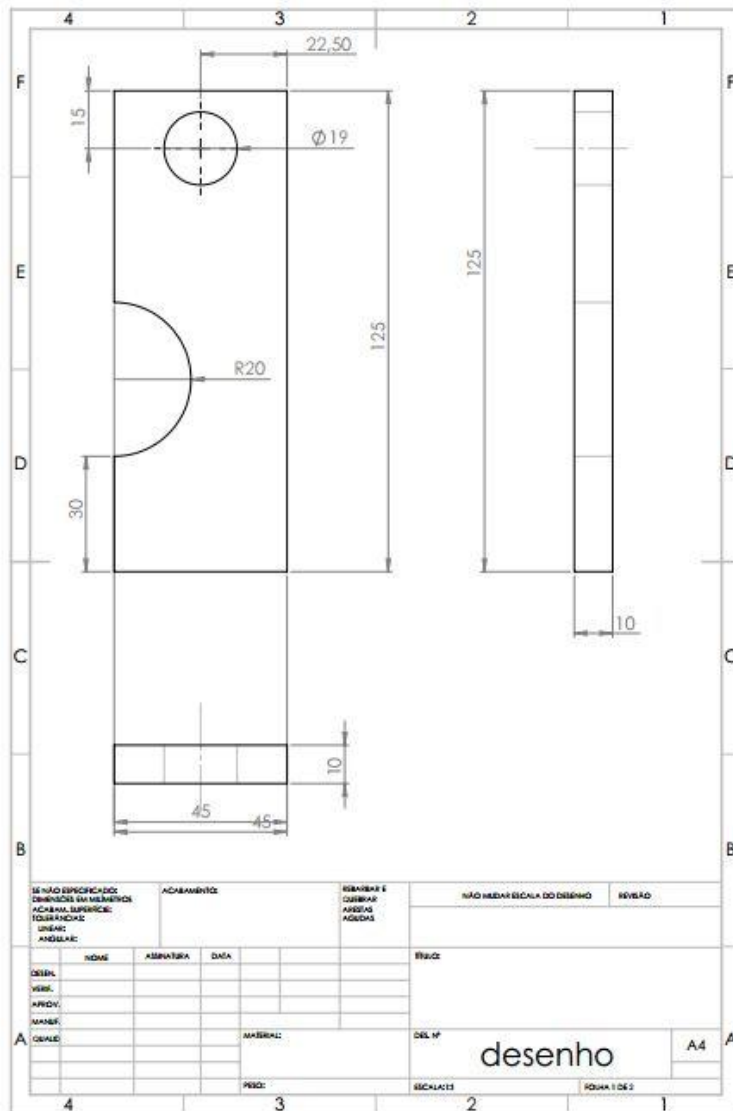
Desenho técnico do suporte do sensor indutivo.
